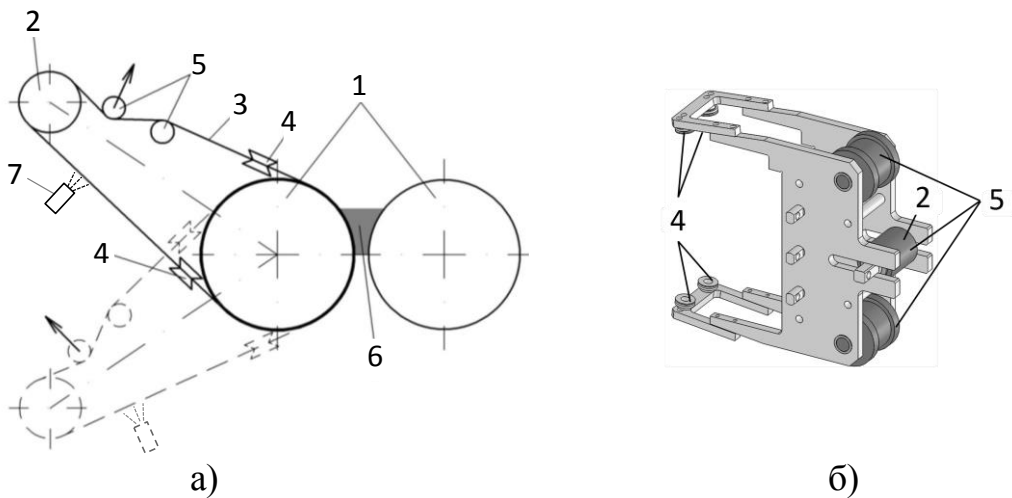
Схема запатентованого пристрою валкового розливу-прокатки профільованих штаб (а) та тривимірне зображення виготовленого пристрою (б): 1 – валок-кристалізатор; 2 – натяжний ролик; 3 – профілююча стрічка; 4 – профільовані ролики; 5 – компенсаційно-натяжні ролики; 6 – метал в зоні кристалізації-деформації; 7 – нанесення розділового шару на профілюючу стрічку
